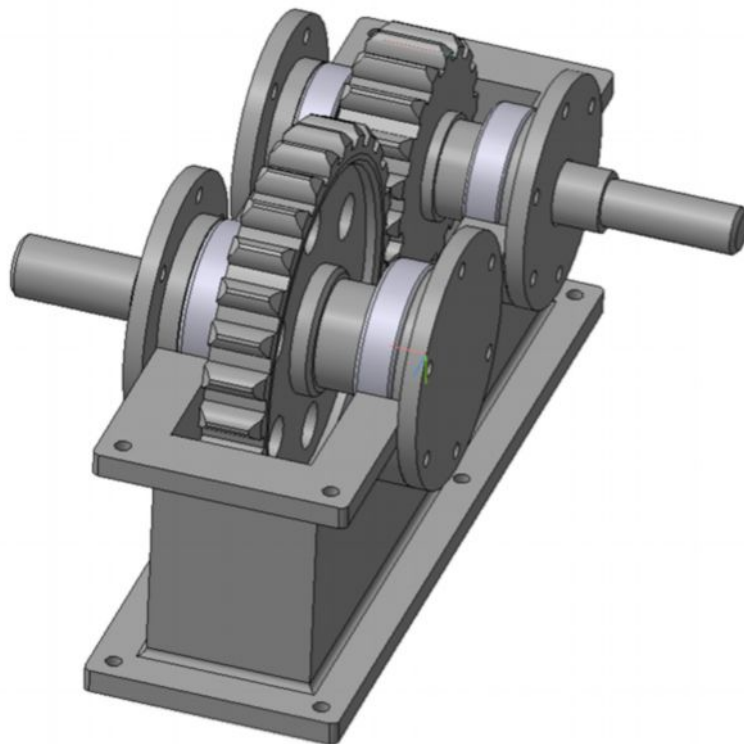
Установка валів з колесами в нижню частину корпуса редуктора
